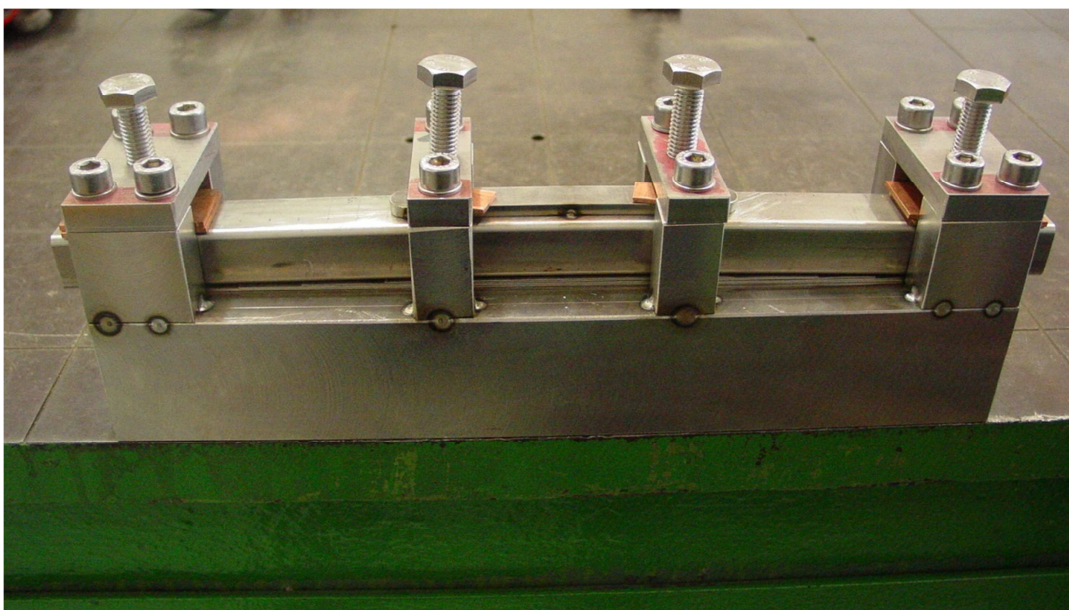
Attrezzatura pre-curvatura He-inlet / *Tool for He-inlet pre-bending
